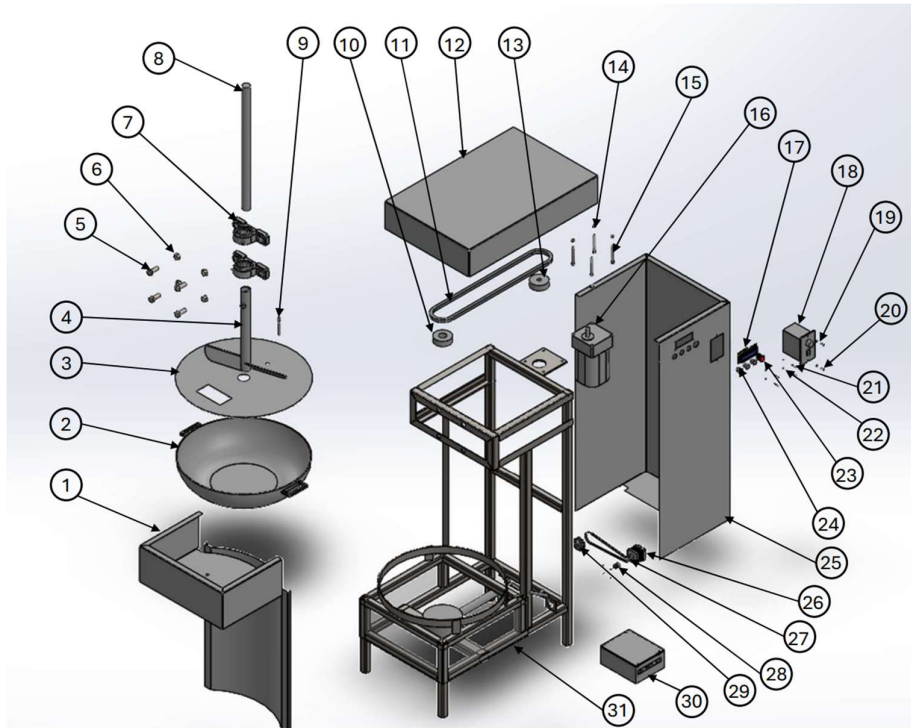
Vista isométrica explosionada de la solución seleccionada
